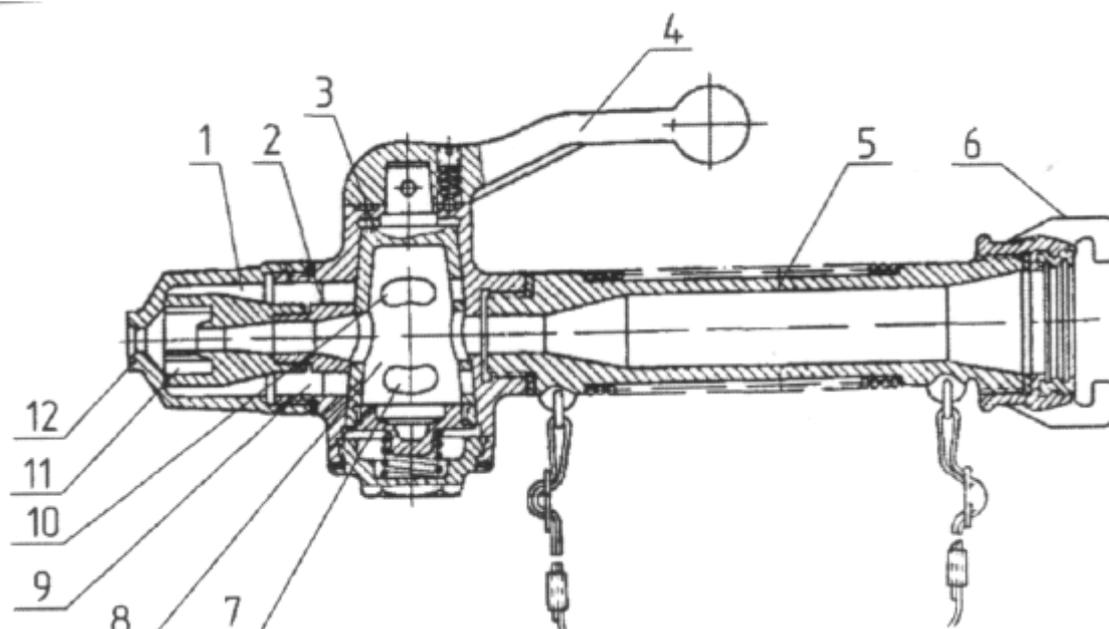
Ручной пожарный ствол РСК-50 (1,2,9 – каналы; 3 – пробковый кран; 4 – ручка; 5 – корпус; 6 – соединительная головка; 7,10 – отверстия; 8 – полость; 11 – тангенциальные каналы; 12 – насадок)
